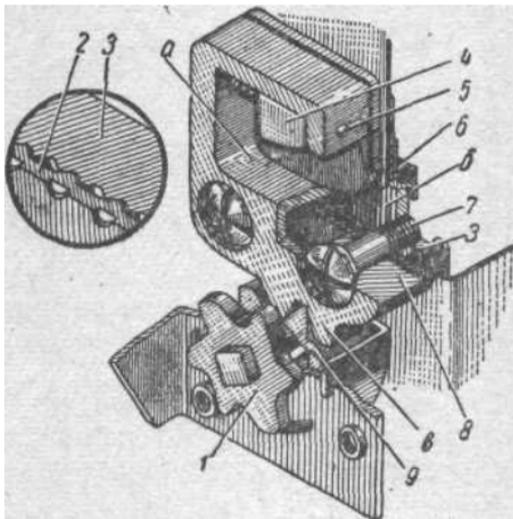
Зашелка замка двери и сопрягающиеся с ней детали замка:
